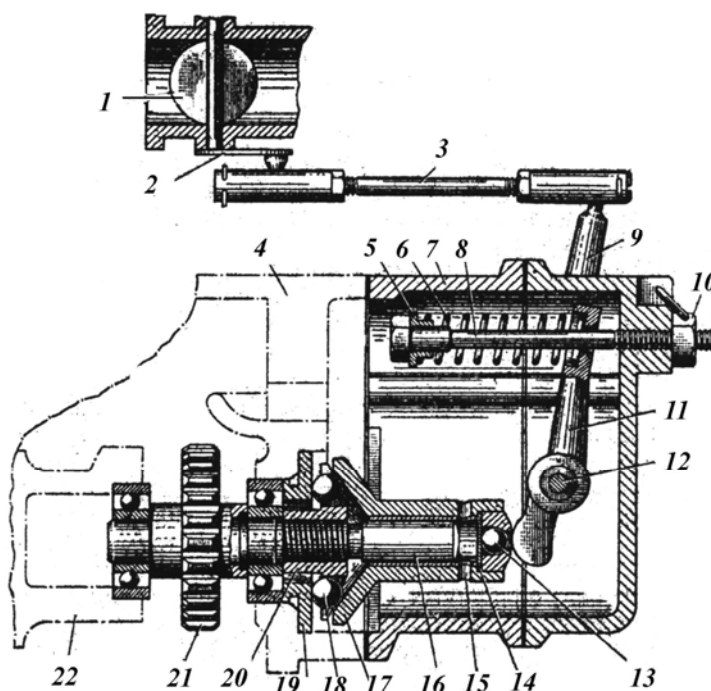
Однорежимный шариковый центробежный регулятор пускового двигателя:
